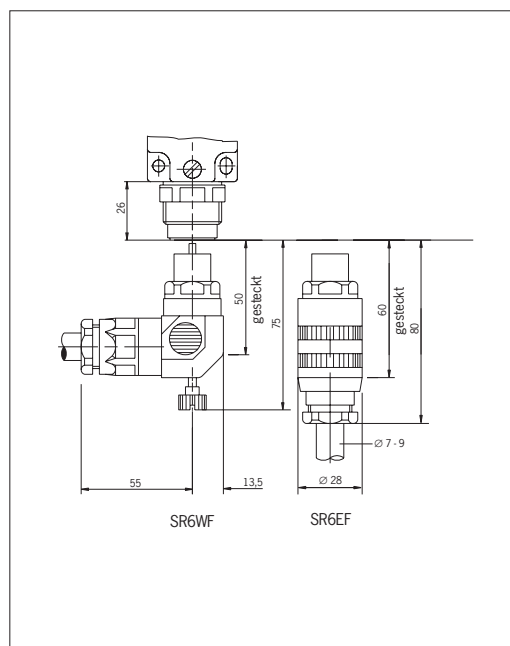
Maßzeichnung NG2... mit Steckverbinder SR6
